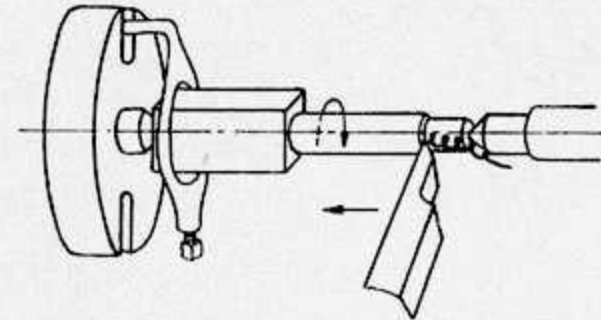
Podélné soustružení, materiál upnut ve hrotech.
